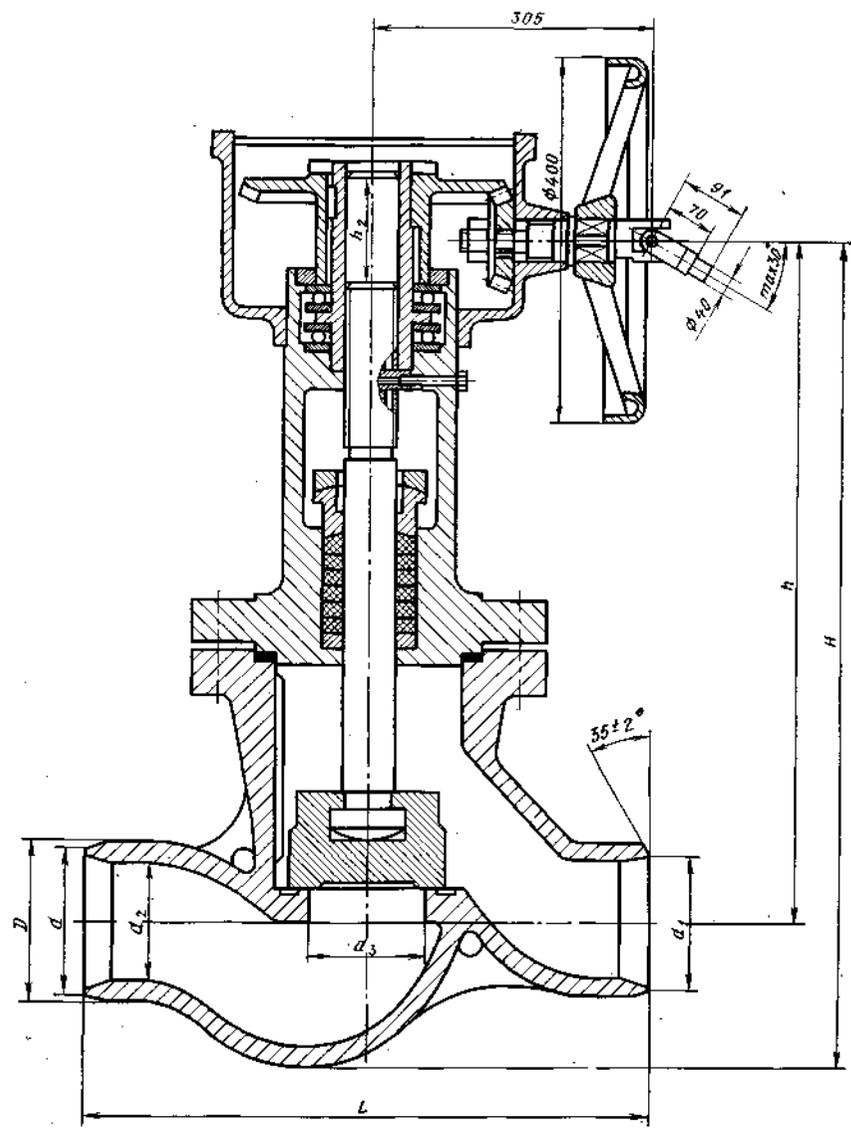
Вентиль 1с-9 с приводной головкой и конической зубчатой передачей D_v 80
